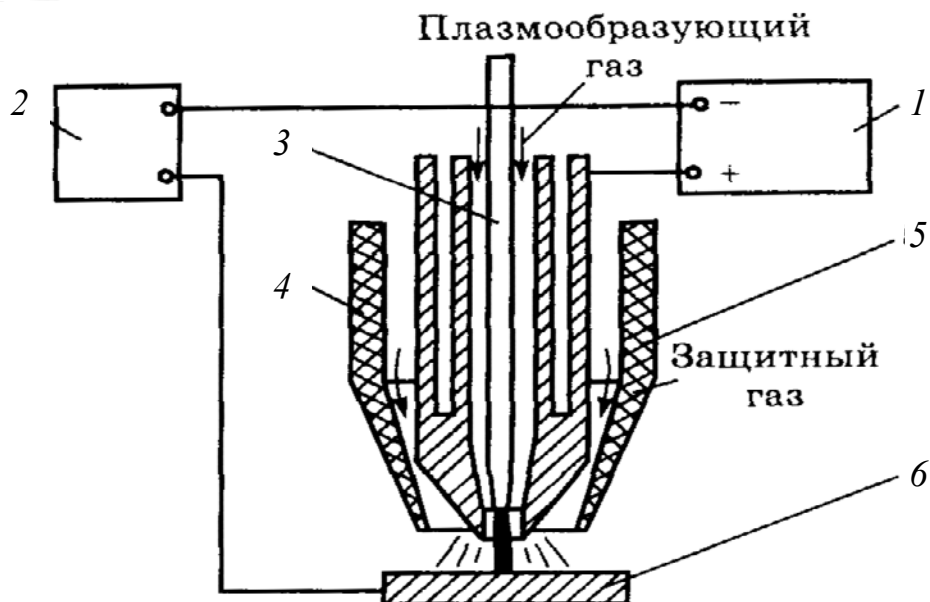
Схема процесса микроплазменной сварки
